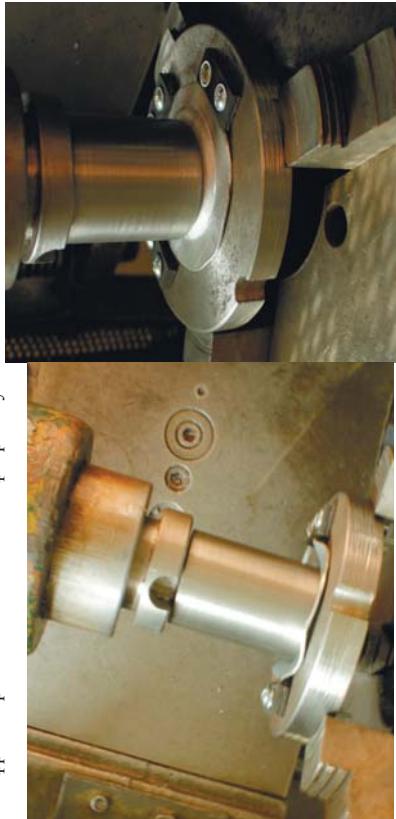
Витягування заготовки з фланцевою частиною: а) – перший переход з отриманням гофрів;
